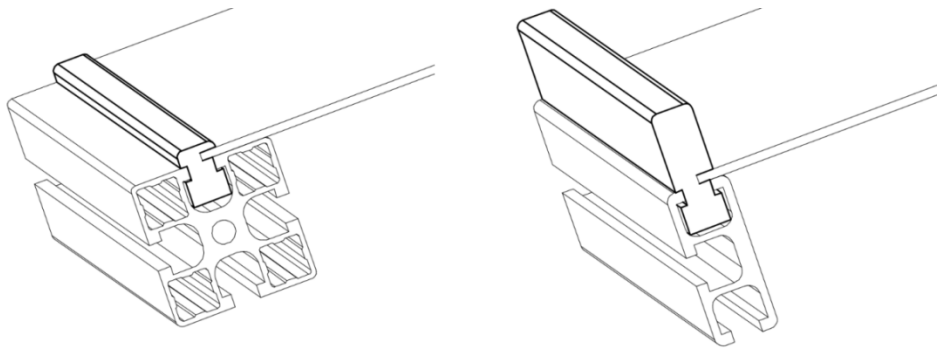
Upevňovací desky ALUTEC K&K s.r.o. [12]
